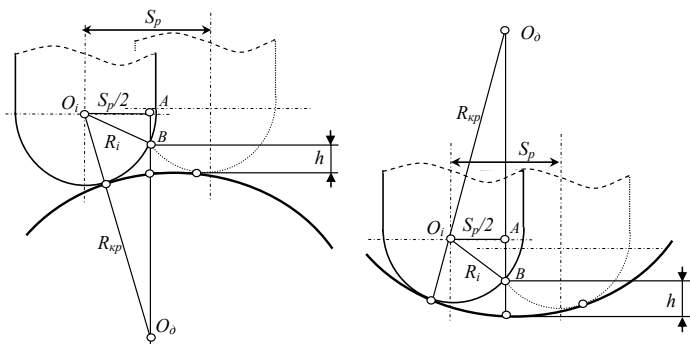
Схема геометрического взаимодействия инструмента и обрабатываемой поверхности [2]
